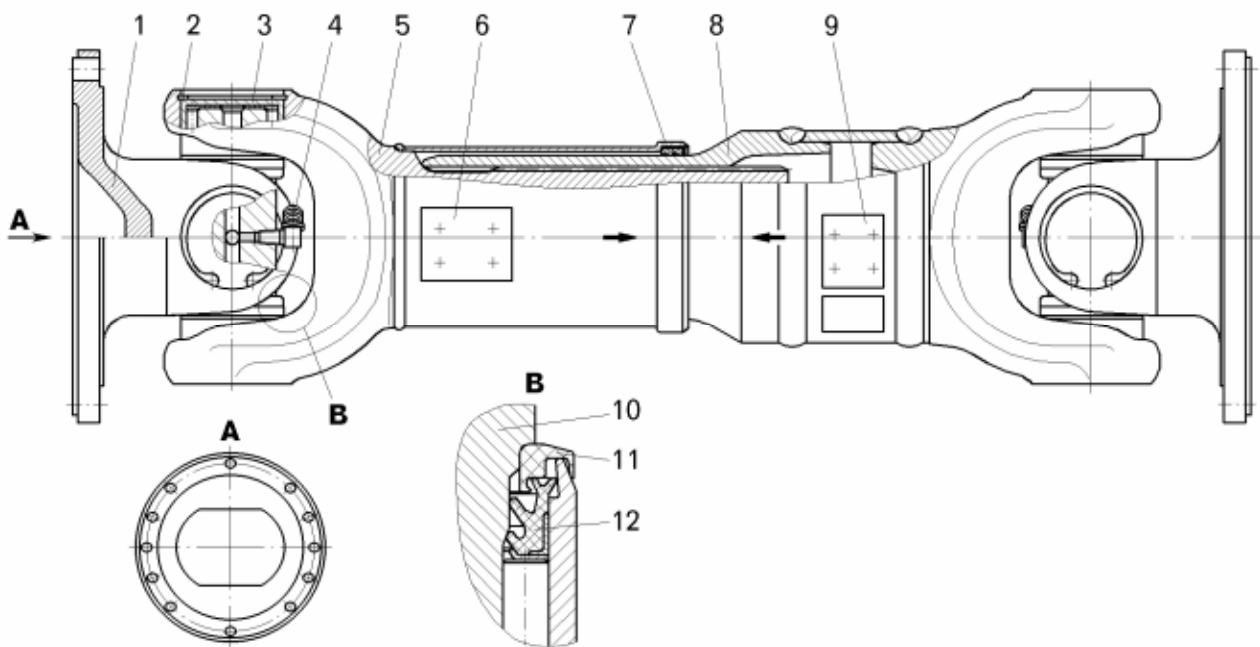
Карданный вал гидромеханической передачи:
